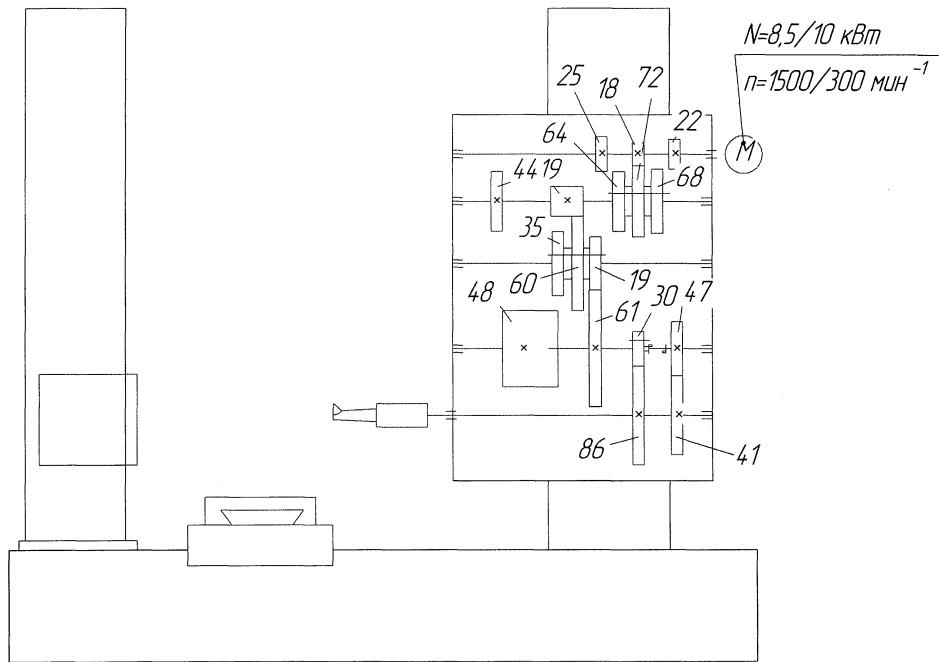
Кинематическая схема коробки скоростей станка 2620
